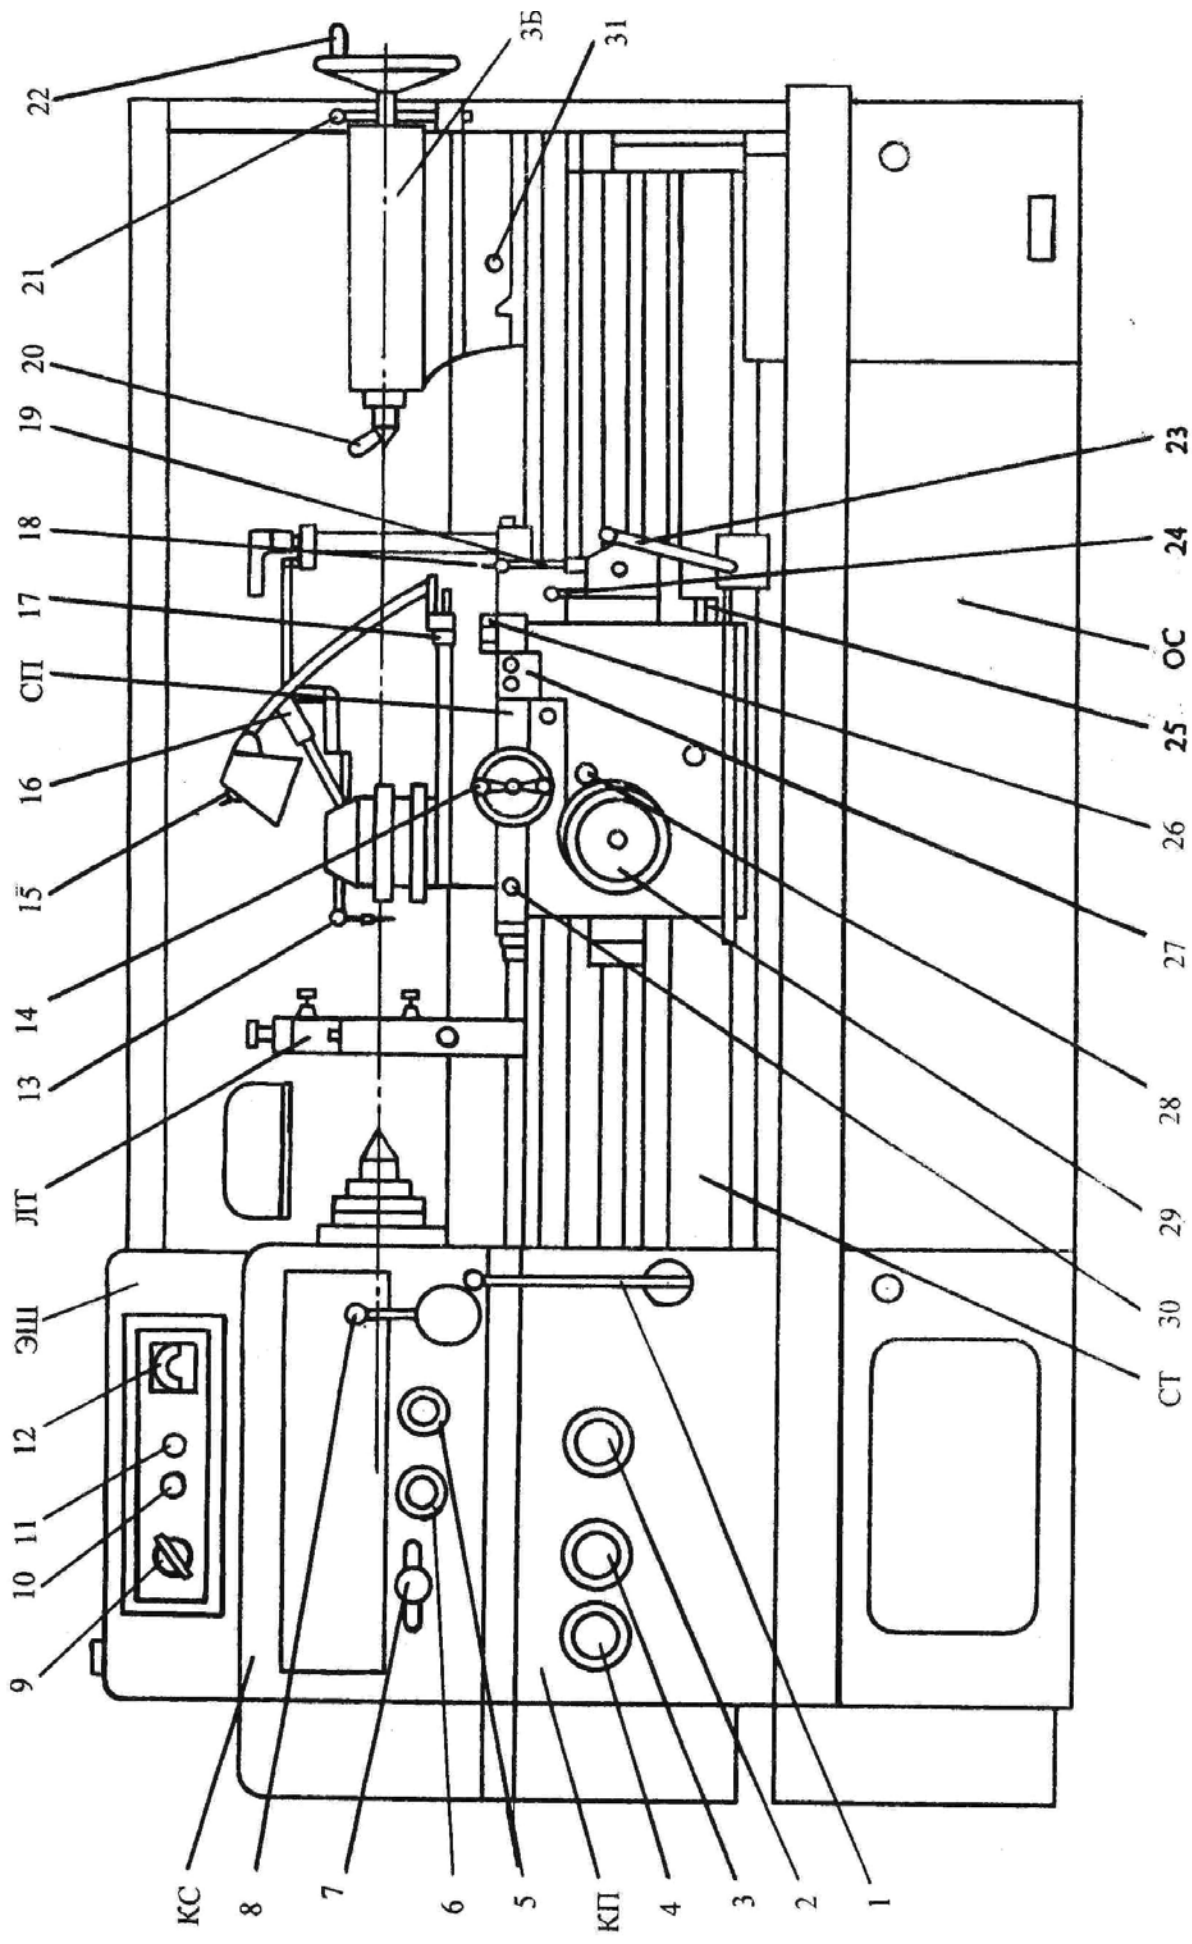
Основные части и органы управления токарно-винторезного станка модели
